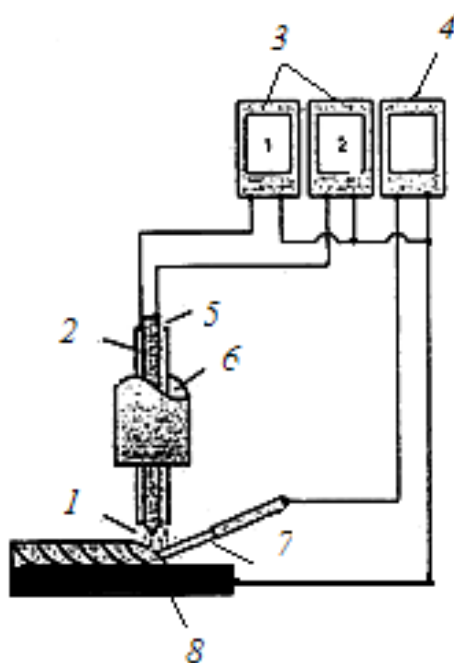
Схема процесса двухдуговой сварки ТИГ:
